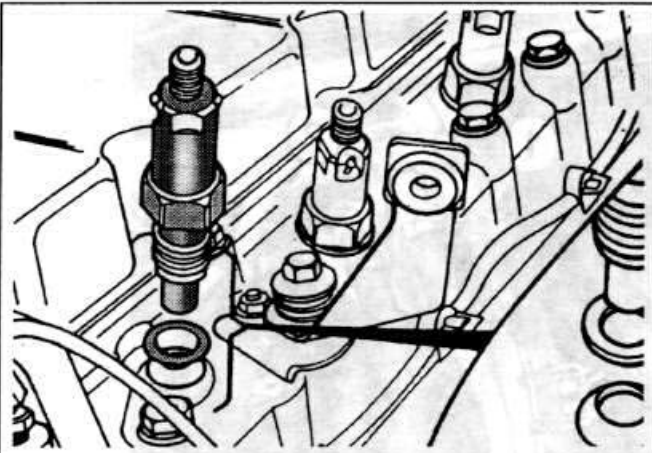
Положение уплотнительных колец при установке форсунок
